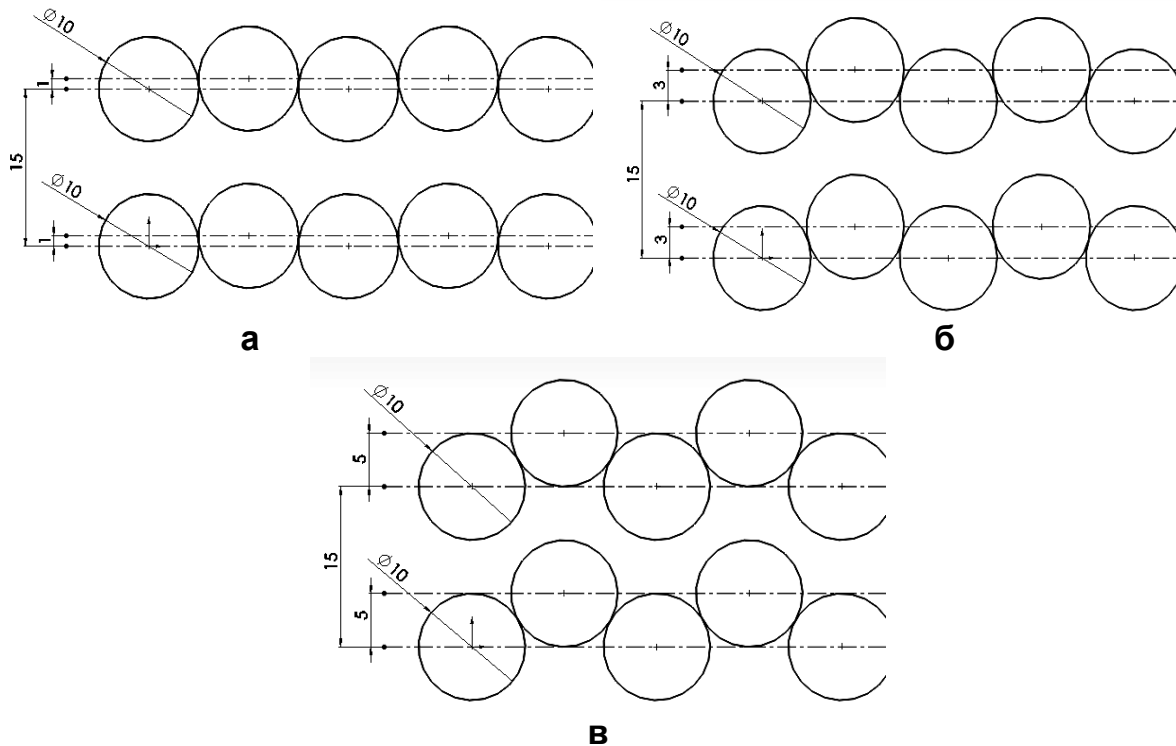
Розташування компактного пучка труб (вигляд зверху):
